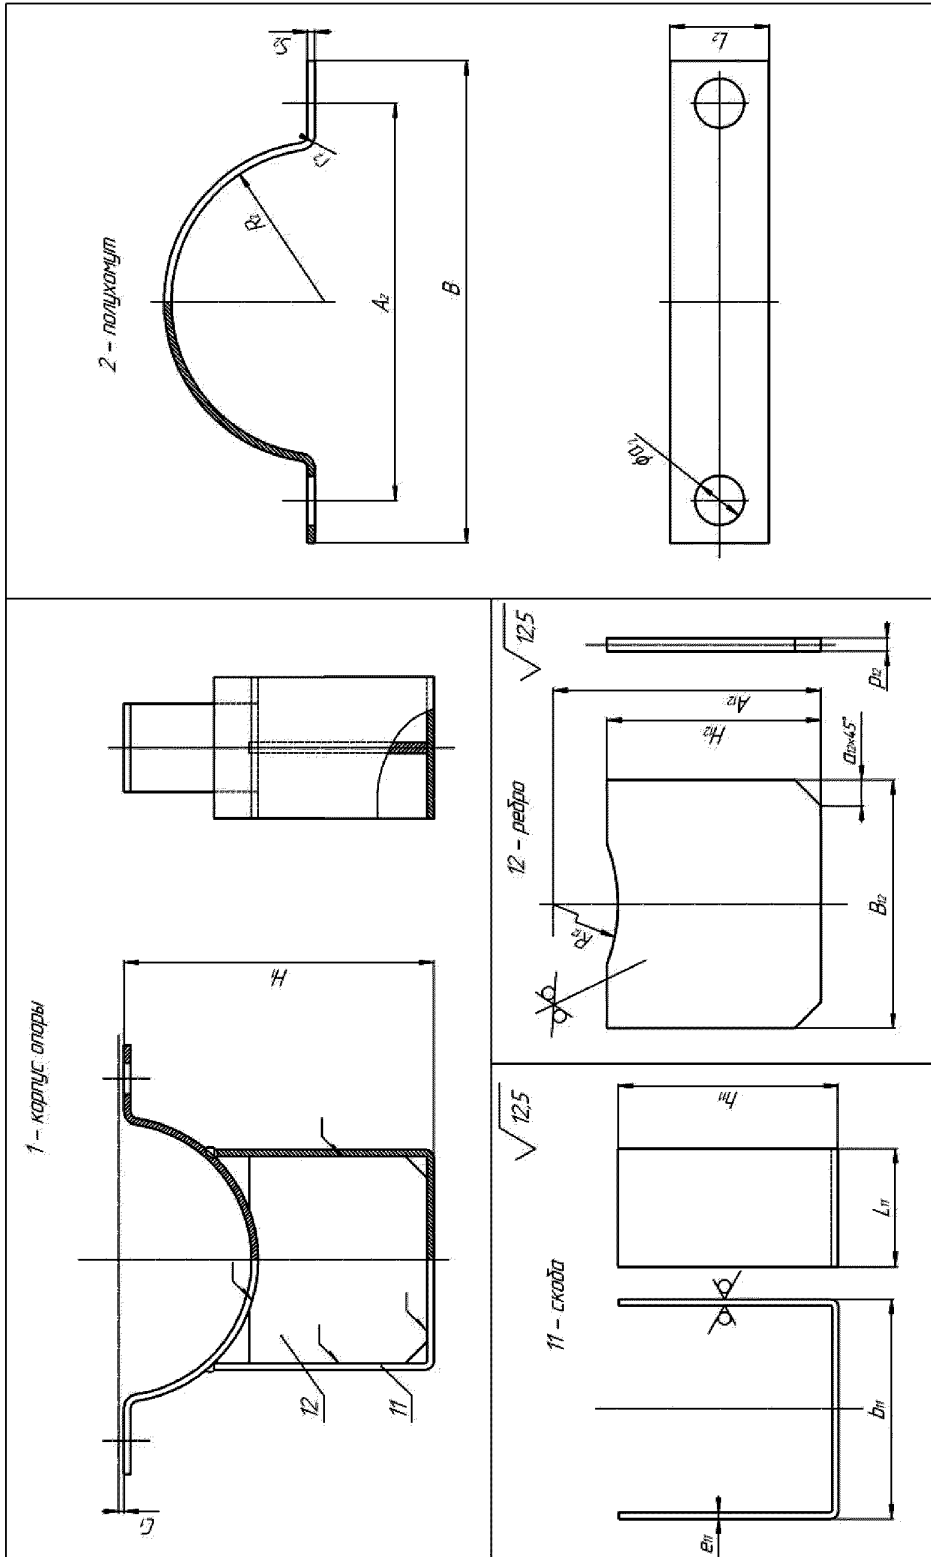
Детали изделий 01-XXXXX-S-1С-03-А, 01-XXXXX-S-1С-04-А и 01-XXXXX-S-1С-01-В для  $D_H=57 \div 219$  мм
